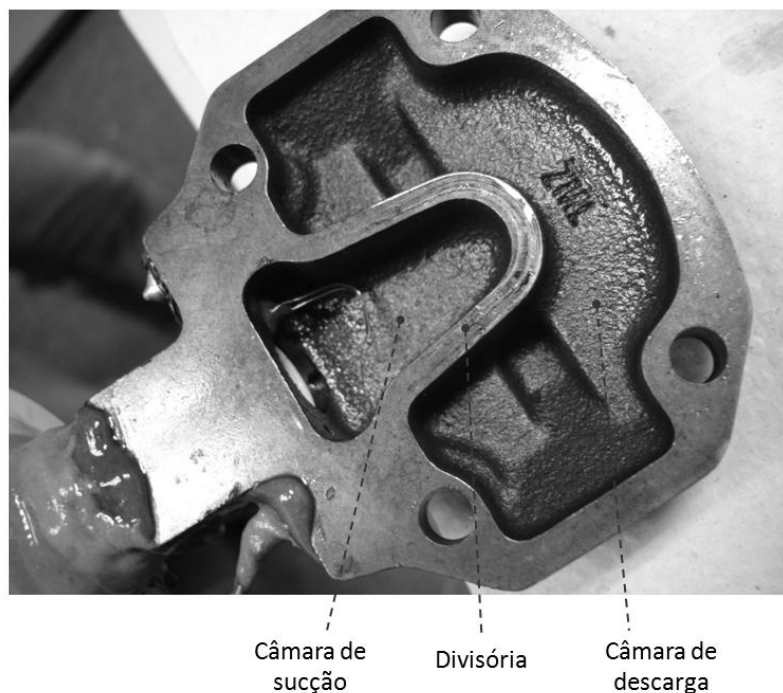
Tampa do cilindro de compressão e suas partes.
